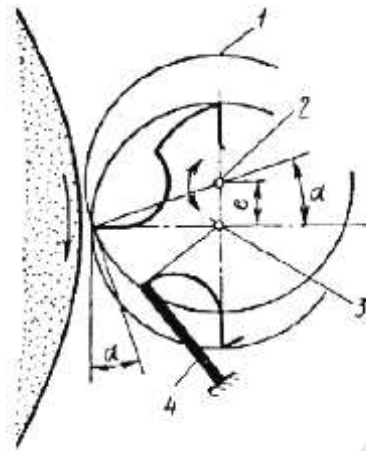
Схема затылования: 1 – цилиндр затылования; 2 – ось качания в центрах станка; 3 – ось метчика; 4 – упорка
